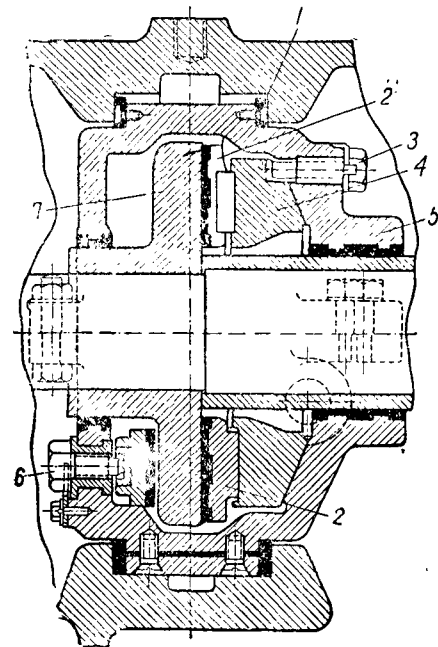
Одногребенчатый упорный подшипник ЛМЗ.
